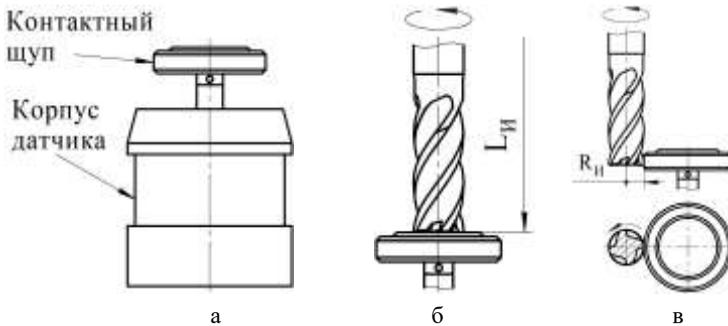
Настройка НИ на фрезерном станке: а – датчик для настройки; б – настройка длины; в – настройка радиуса режущей части
